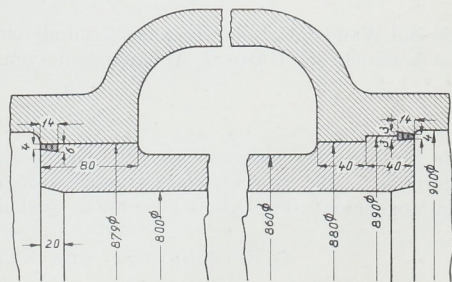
Befestigung und Abdichtung des Laufzylinders im Mantel, Abb. 1745.
